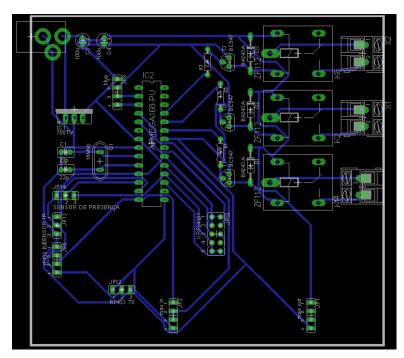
PCB MÓDULO ATMEGA328 FONTE: O AUTOR (2014).
